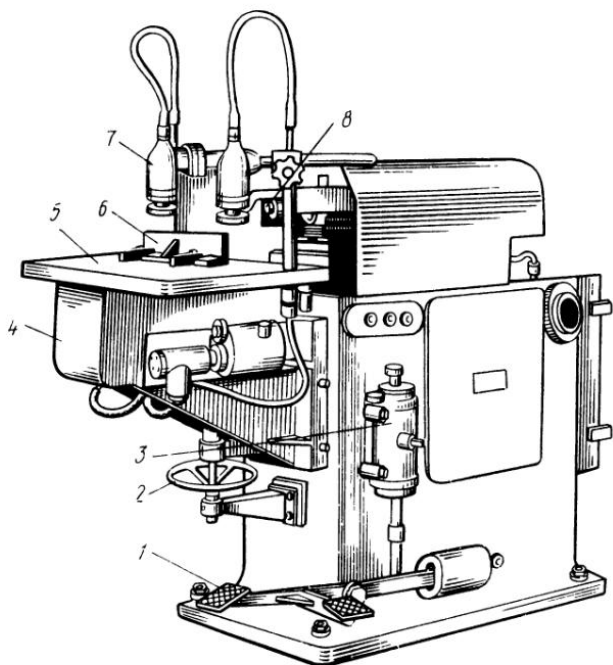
Сверлильно-пазовальный станок СВПГ-2:
